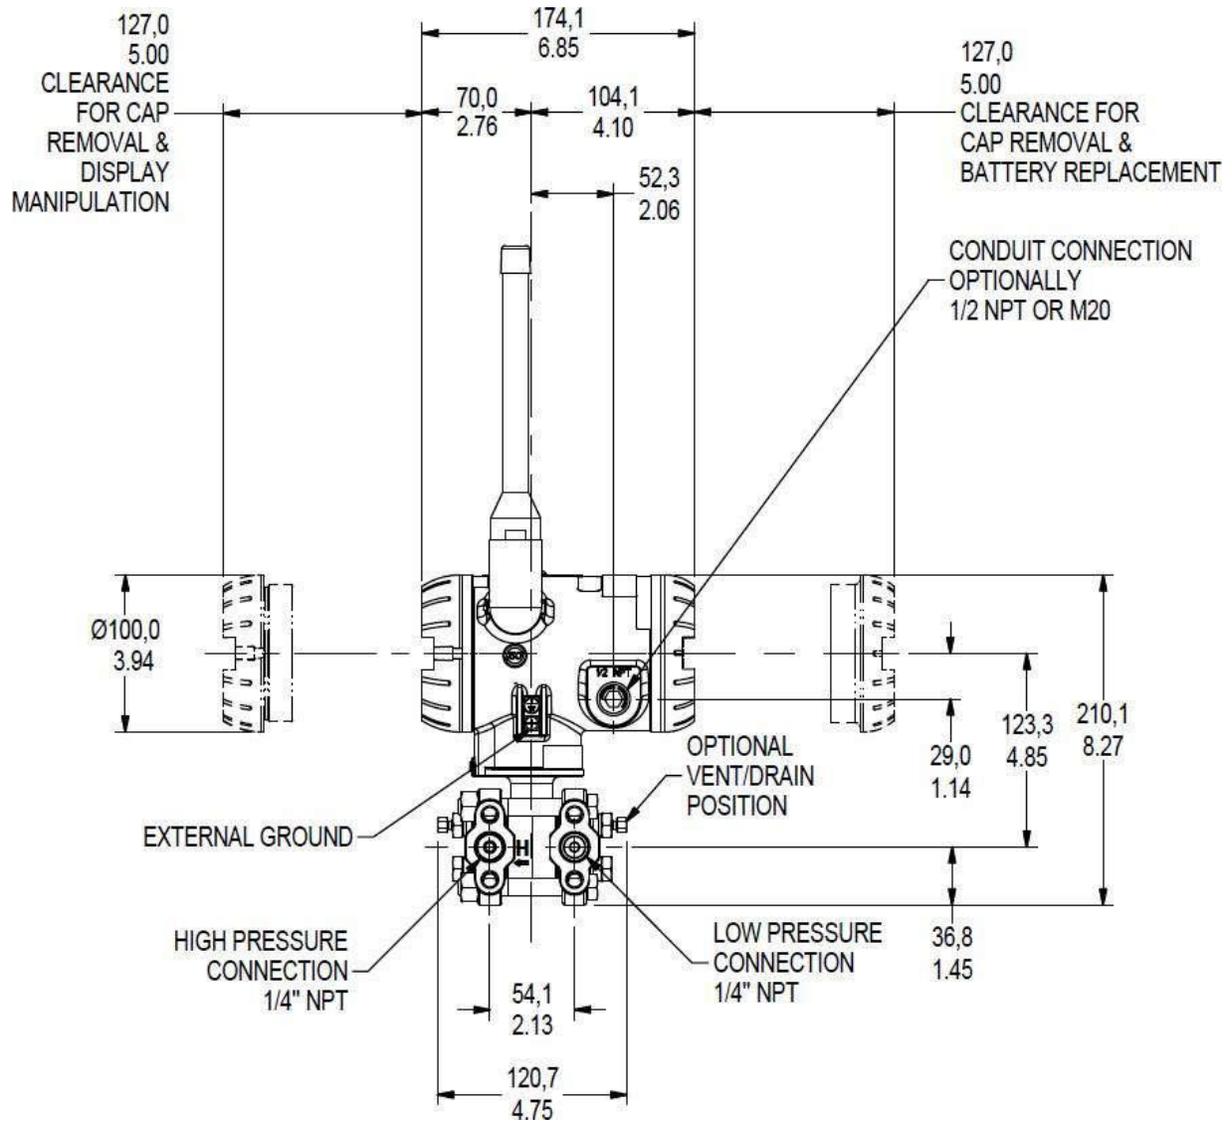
Dessin dimensionnel et informationnel de jauge à deux têtes
